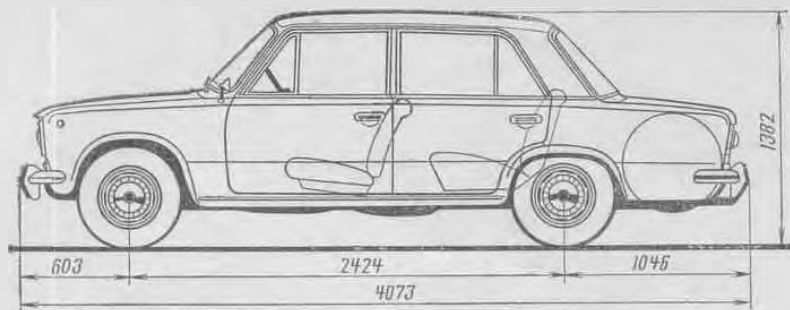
Габаритные размеры автомобиля «Жигули» (ВАЗ-2101)
